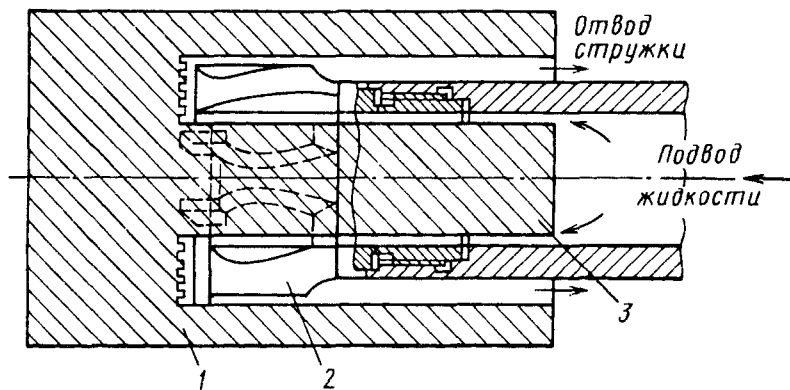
Схема получения заготовки для стержня из отходов при операции рассверливания
